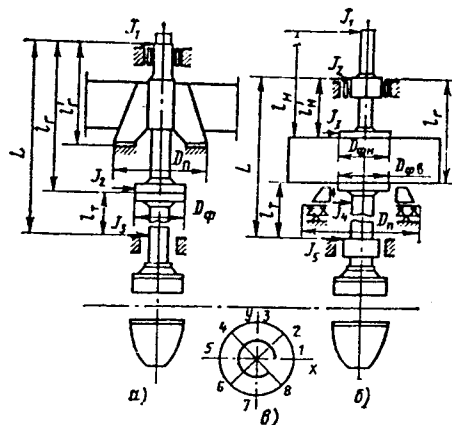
Схема расположения индикаторов для проверки общей линии вала:
